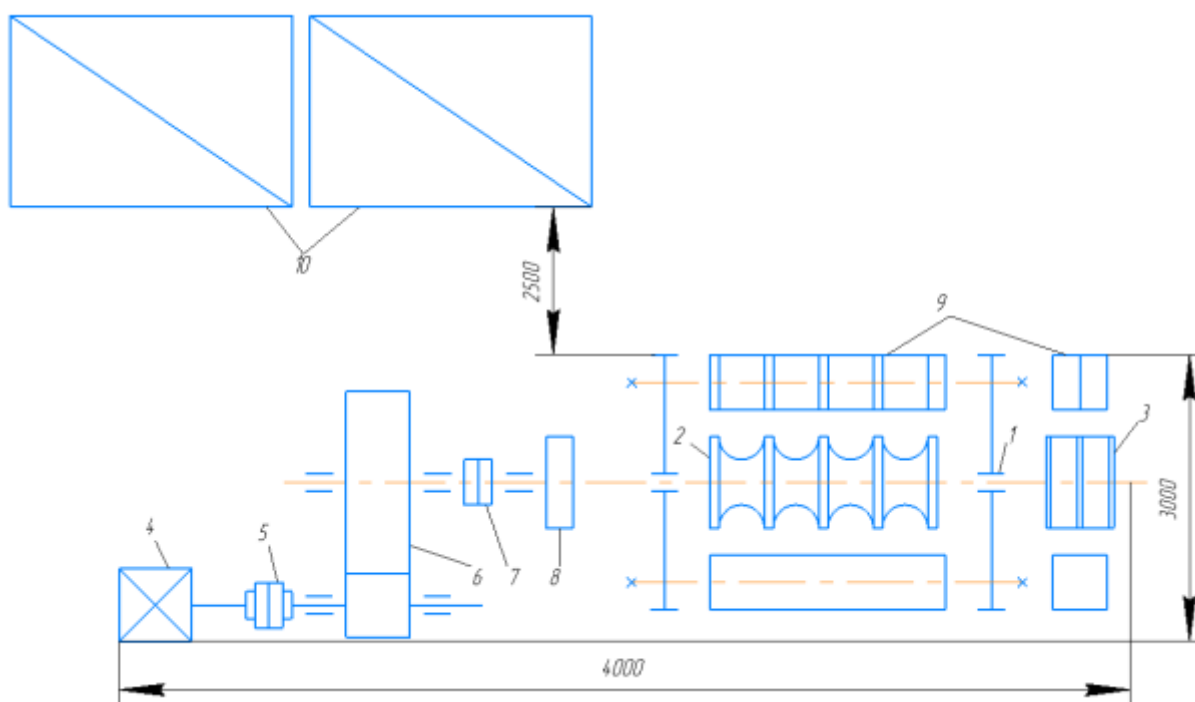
Мини комплекс: 1 - литые станины закрытого типа; 2 – валки; 3 – бандаж; 4 – электродвигатель; 5 – зубчатая муфта; 6 - редуктор; 7 – муфта; 8 – шестерни; 9 - столы; 10 – печи.
